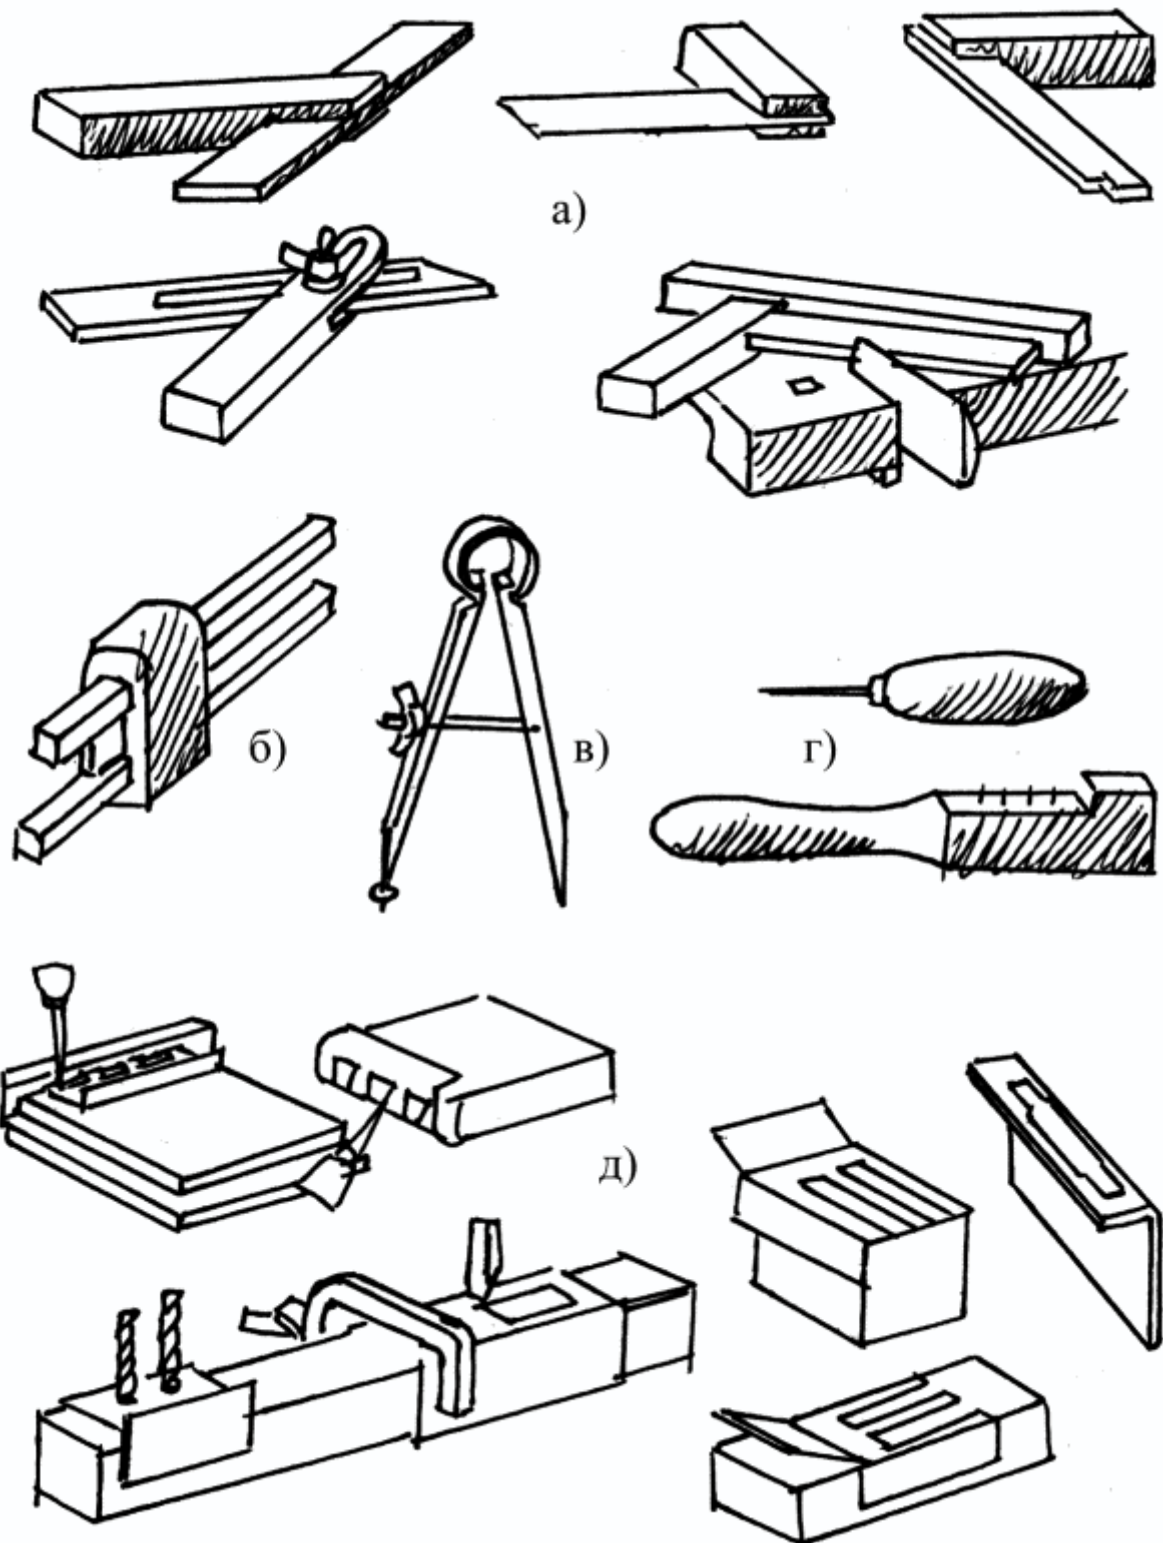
Разметочный и измерительный инструмент: а – угольники; б – рейсмус; в – кронциркуль; г – шило и разметочная гребенка; д – разметочные кондукторы
